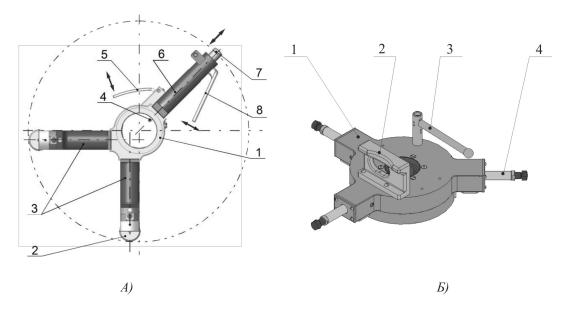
А) Общий вид центроуказателя (без фотоприемника) (а): 1 – втулка; 2 – валик опорный; 3 – опорные ножки; 4 – фиксатор фотоприемника; 5 – рычаг фиксатора фотоприемника; 6 – ножка; 7 – шток; 8 – рычаг штока; Б) Общий вид центроискателя (без фотоприемника) (б): 1 – корпус; 2 – упор для руки; 3 – ручка отвода штоков; 4 – шток
